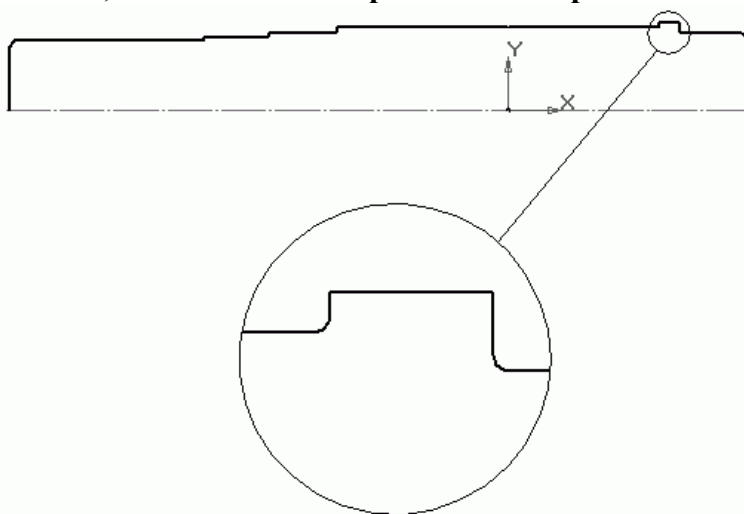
Эскиз вала (скругления показаны увеличенно)
